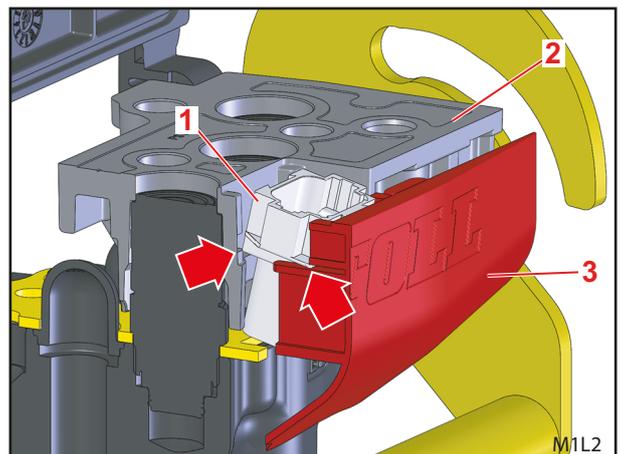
Montare la parte inferiore Hydro-Fix – connettore a spina elettrico e copertura
